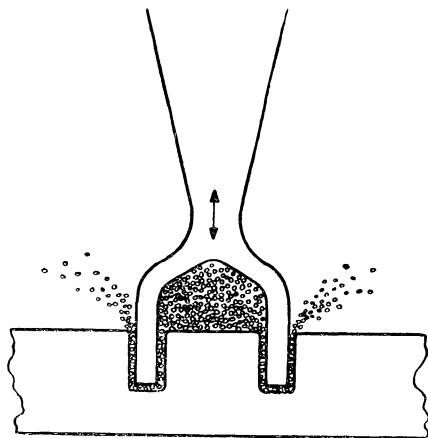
Ультразвуковой инструмент и абразив обрабатывают твердый материал
